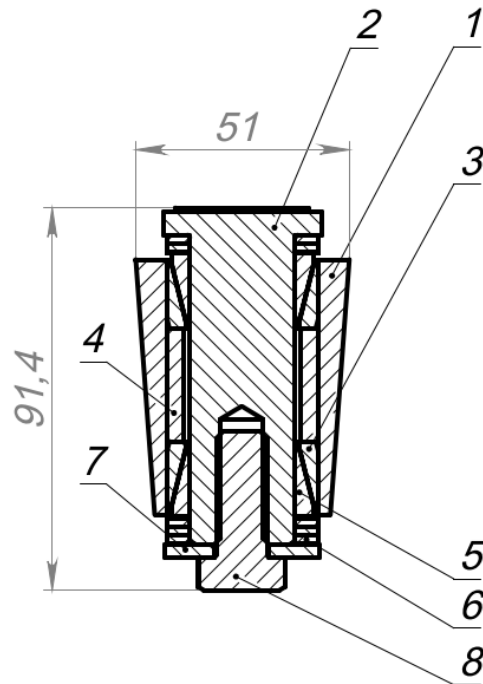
Трибоспряження опорного колеса сошника сівалки Gaspardo MT-8: 1 – важіль опорного колеса; 2 – вісь важеля опорного колеса; 3 – деталь типу «конус» зі сталі; 4 – дистанційна втулка; 5 – деталь із КМ; 6 – регулювальні шайби; 7 – упорна шайба; 8 болт.
